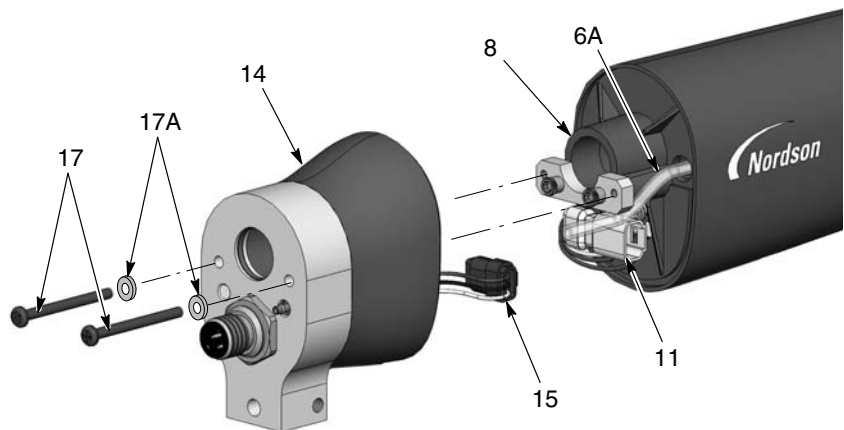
Desmontaje de la pistola de montaje en barra 1 de 3
